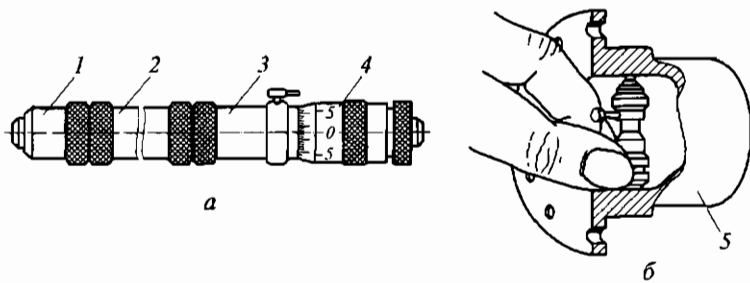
Микрометрический нутромер (а) и определение им посадочных размеров ступицы полумуфты электродвигателя (б):
